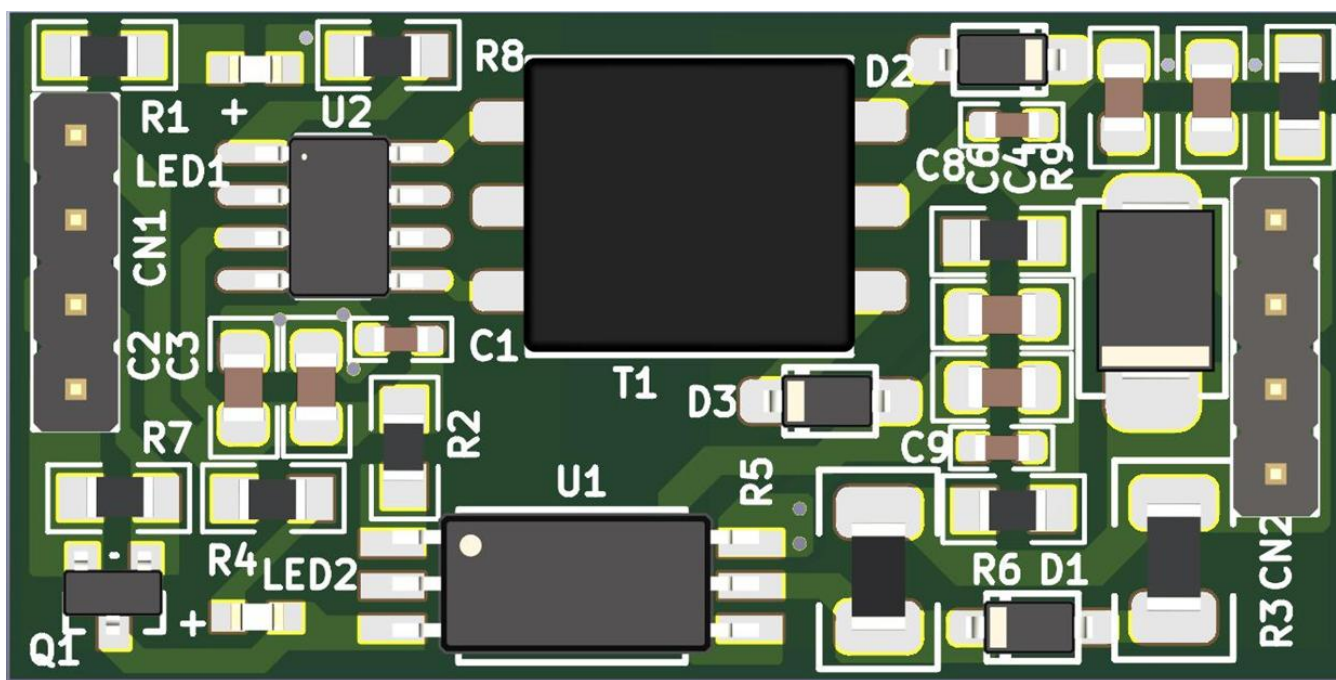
PCB 示意图 (尺寸: 40 x 20mm)
